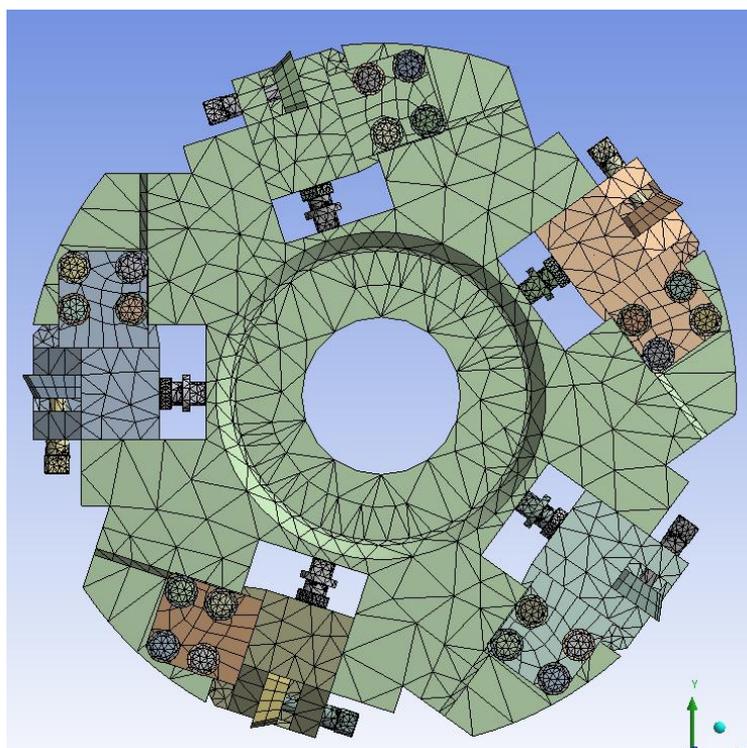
Конечно-элементная модель фрезы (вид снизу)
